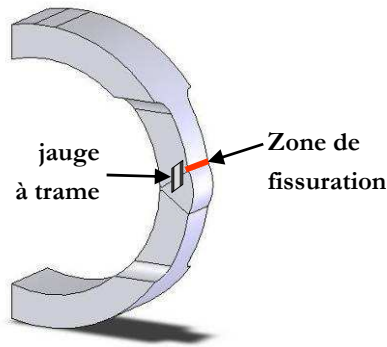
site d'amorçage des fissures sur maquette soudée
